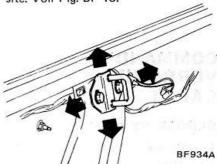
Réglage de la gâche de couvercle de coffre
